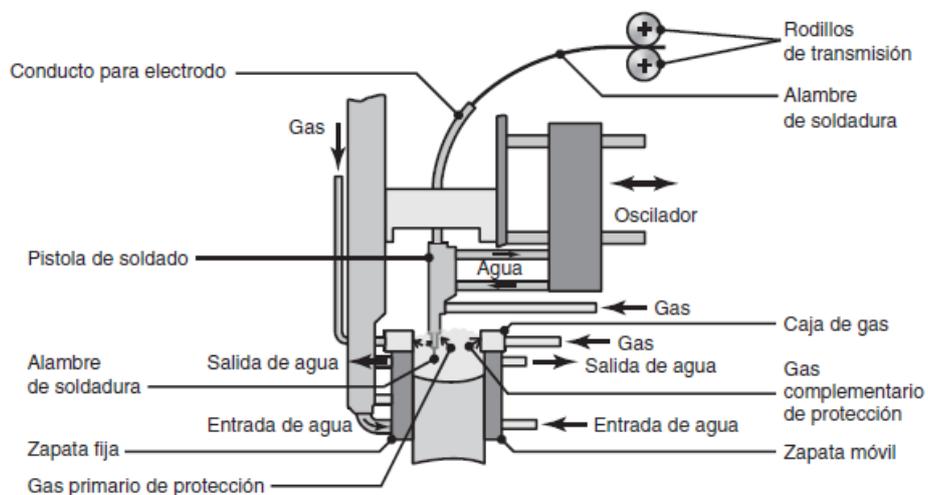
Soldadura con electroescoria (Fuente: Manufactura, Ingeniería y Tecnología)
